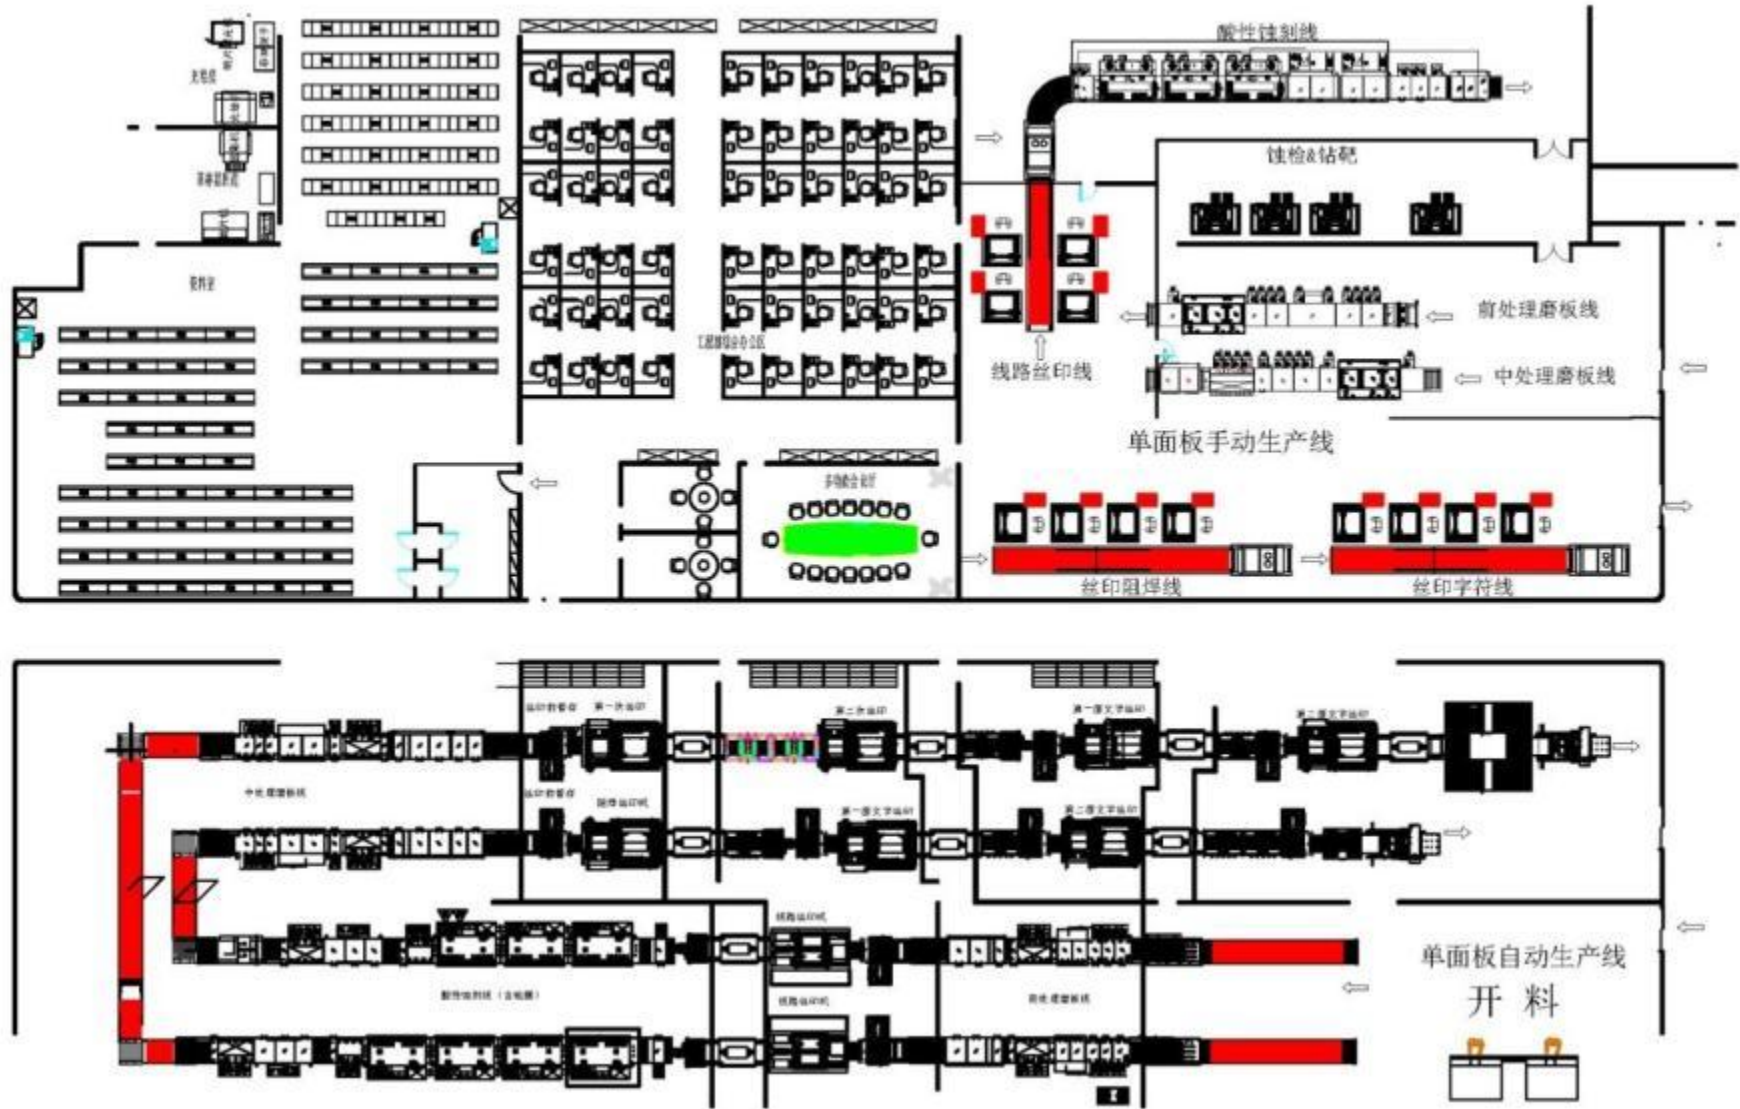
本项目二号厂房 4 楼环评阶段平面布置图
